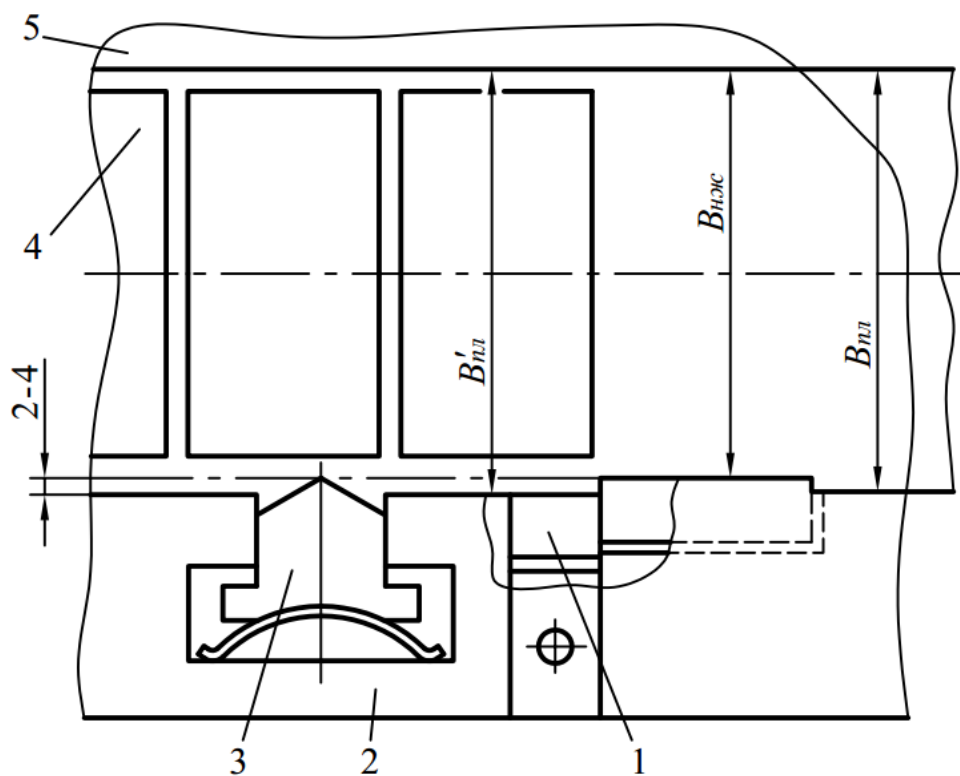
Конструкція напрямної планки з кроковим ножом і бічним притискувачем: 1 – упор крокового ножа; 2, 5 – напрямні планки;
